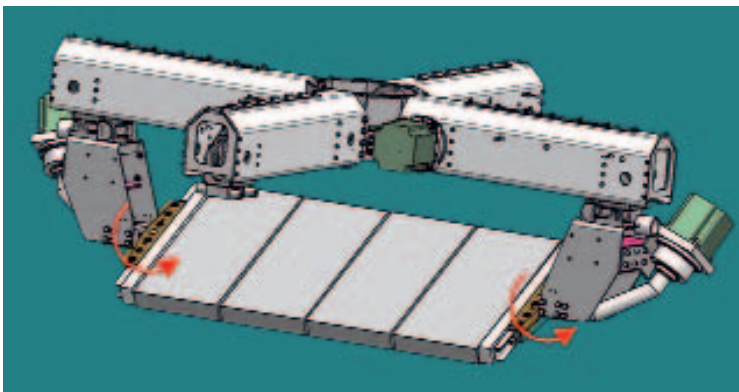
Сборочный чертеж захватного механизма с поворотными захватами.
